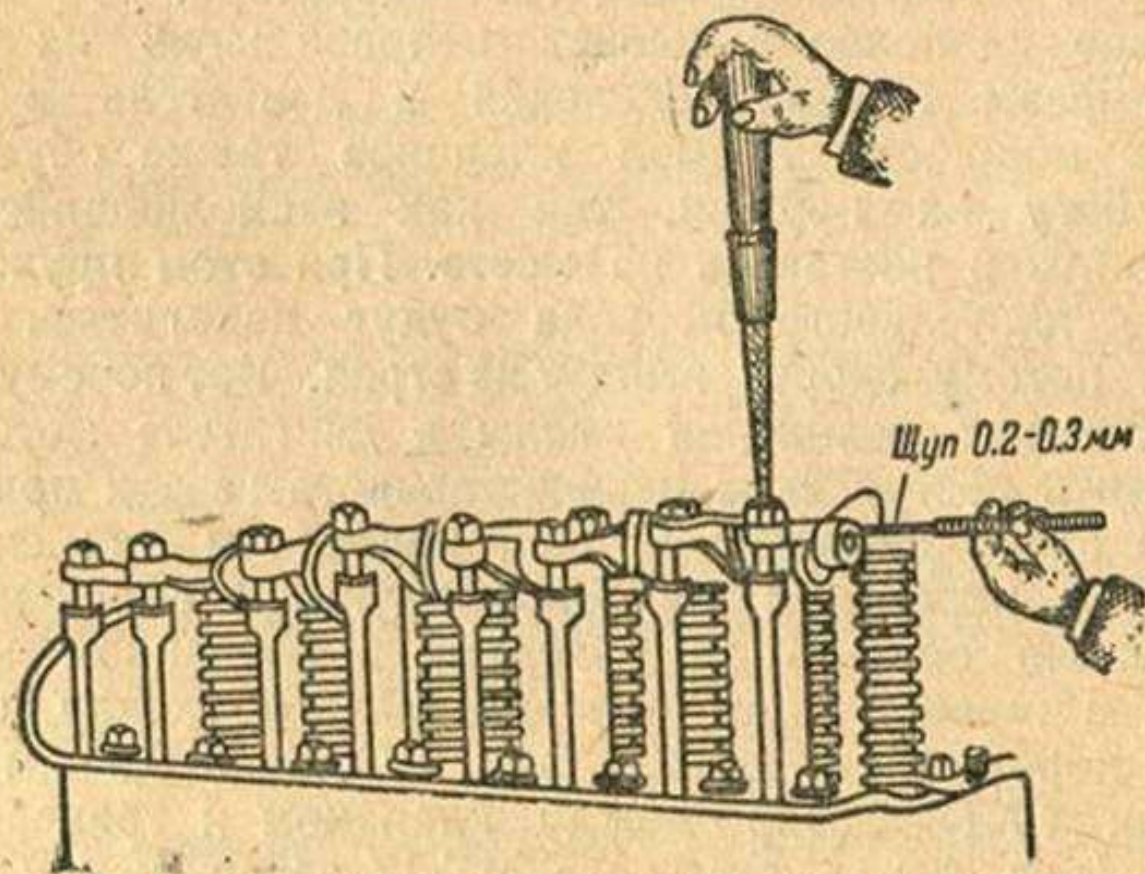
Регулировка зазоров клапанов у двигателя СХТЗ-30
